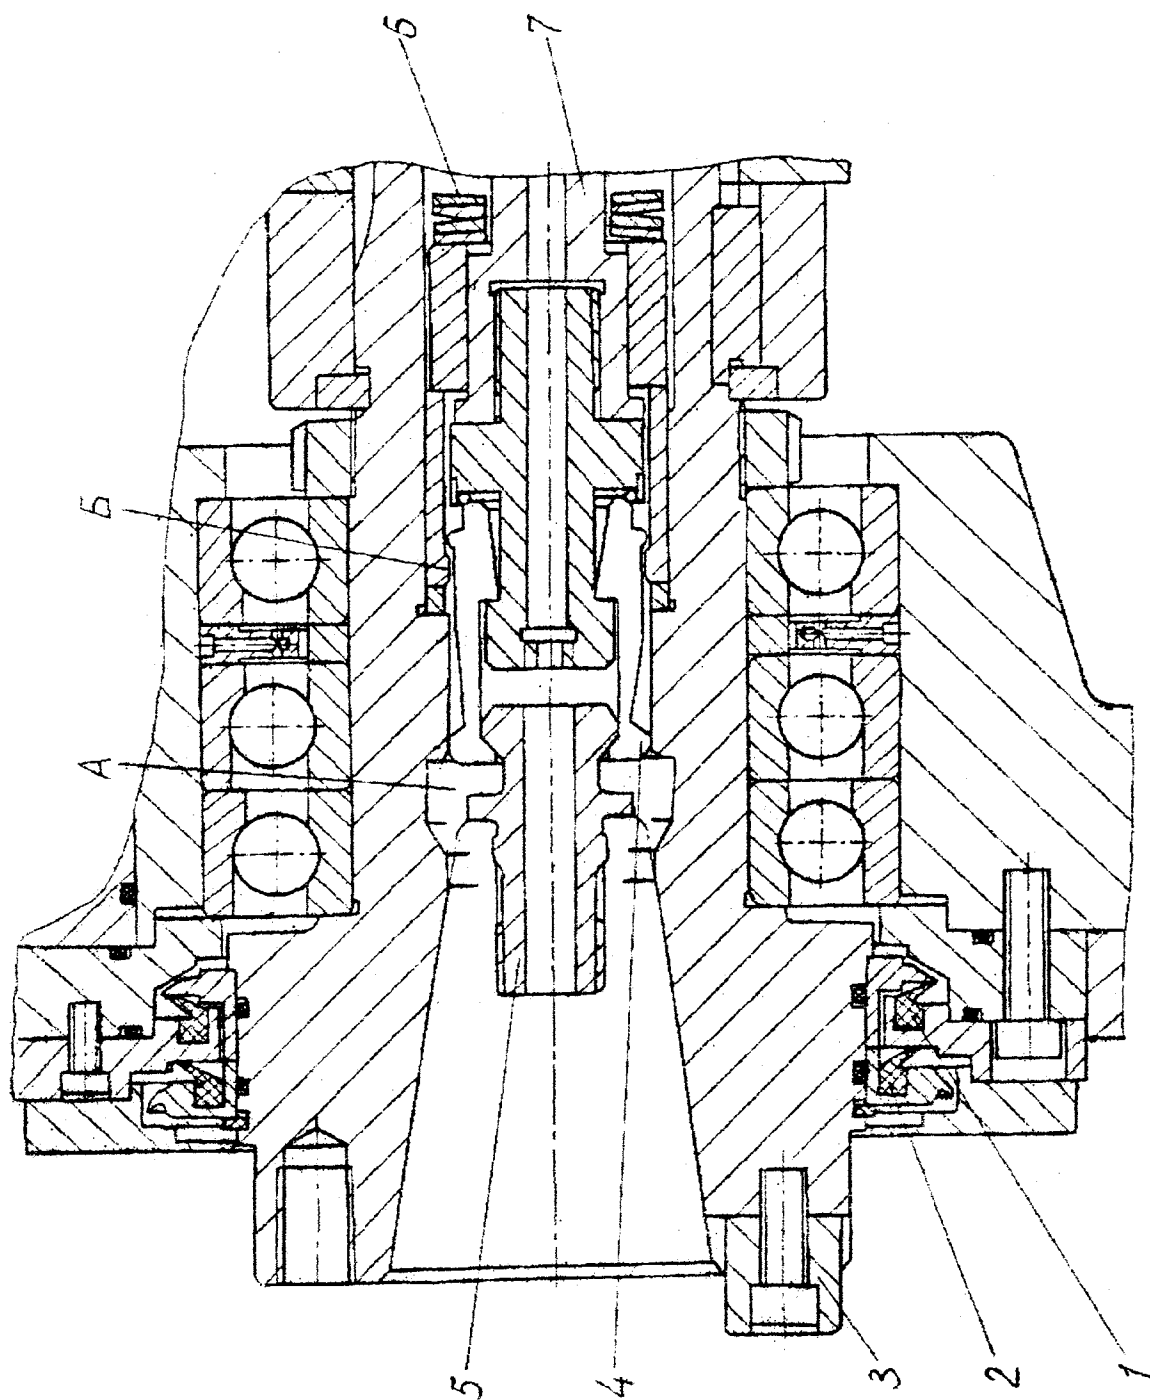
Шпindelный узел многоцелевого фрезерно-сверлильно-расточного станка
